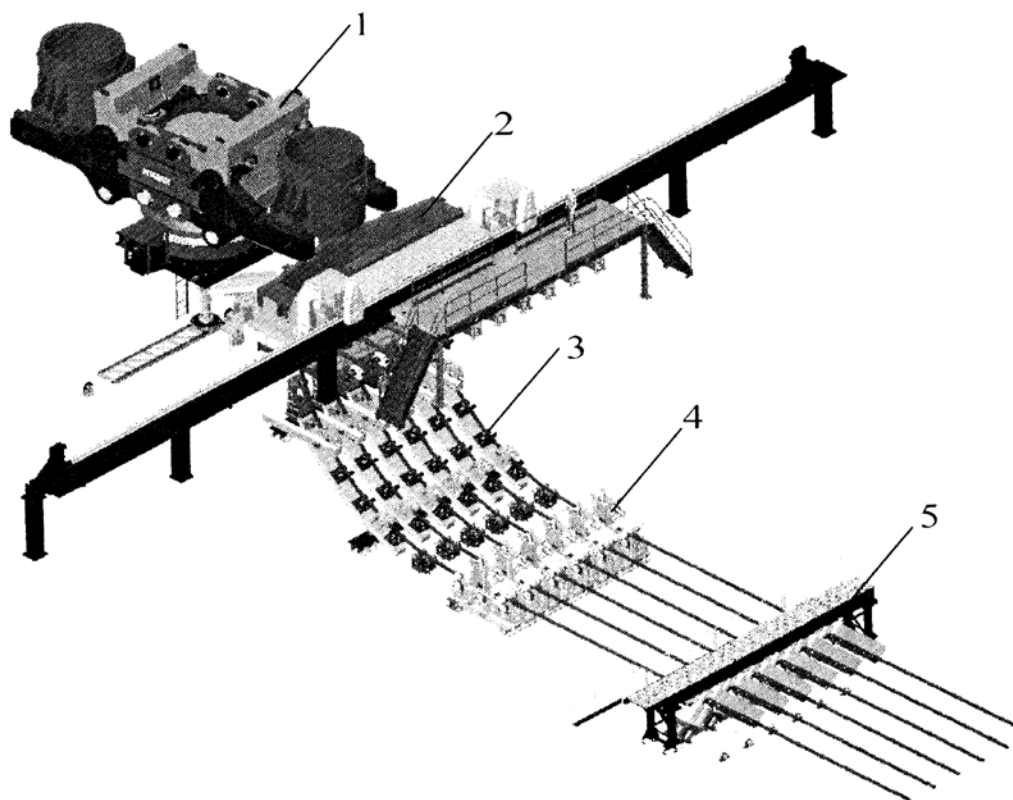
Схема радиальной сортовой МНЛЗ (1 – поворотный стенд со сталеразливочными ковшами, 2 – проковш, 3 – разливочная дуга и ЗВО, 4 – тянуще-правильная машина, 5 – устройство для порезки заготовки)
